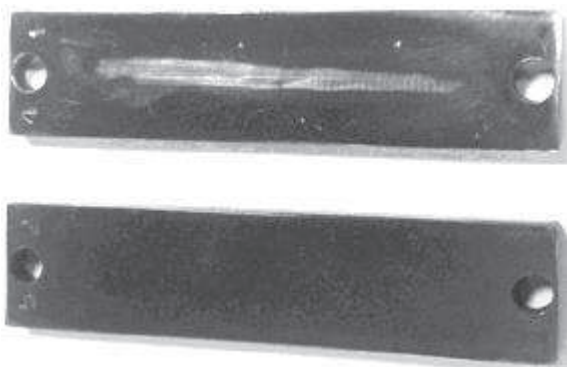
Исходный образец (сверху) и образец с нанесённым покрытием ФАБО (снизу)
